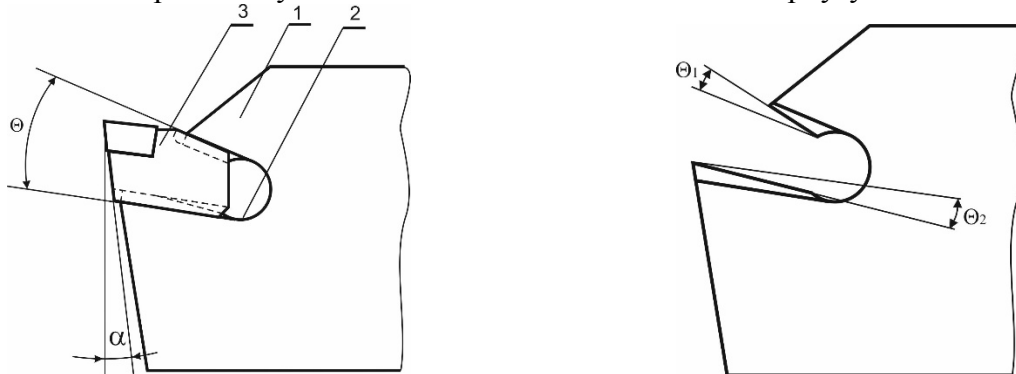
Конструкція збірного відрізнного різця для важких верстатів
